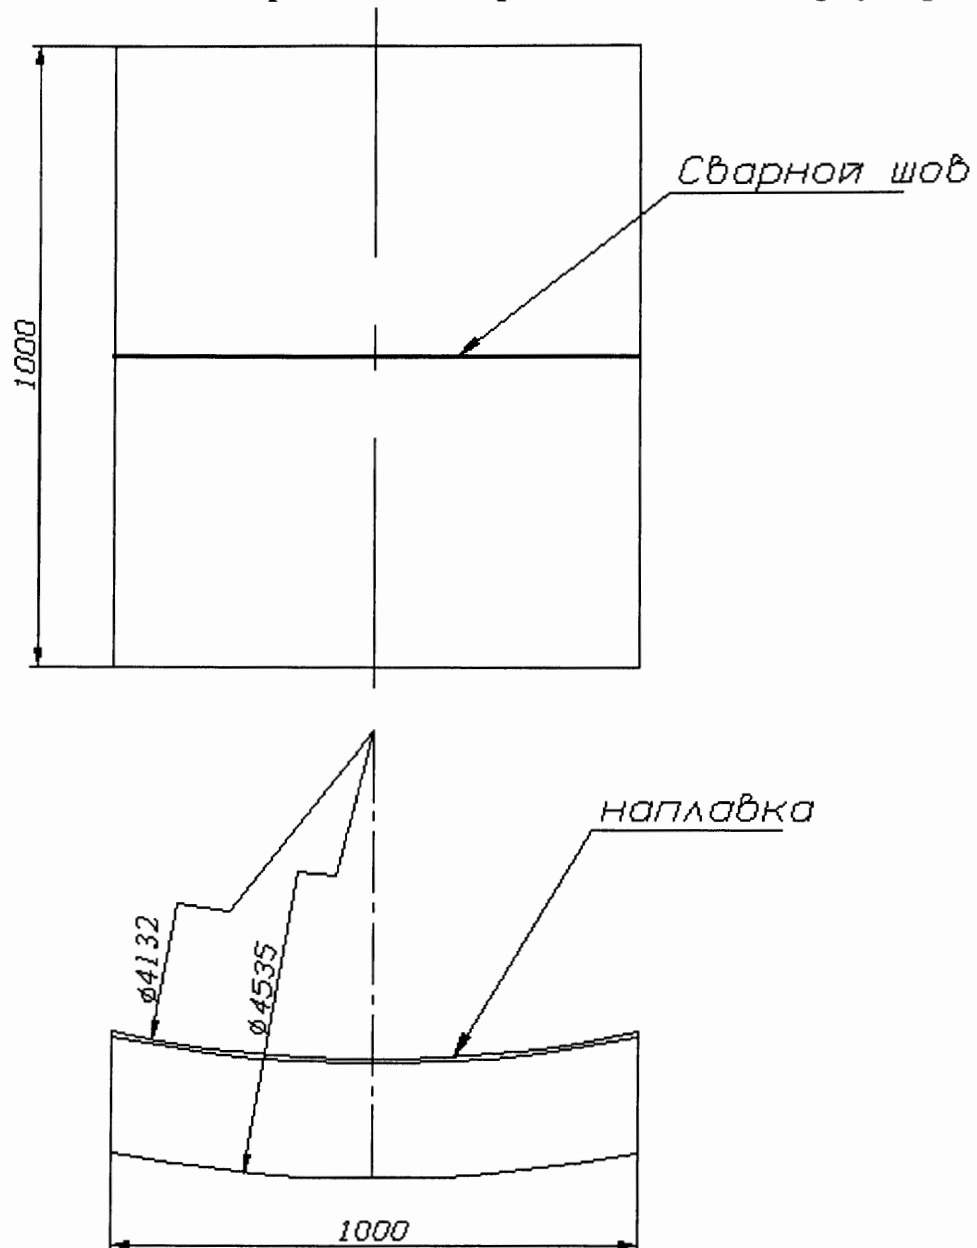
Испытательный образец цилиндрической части корпуса
